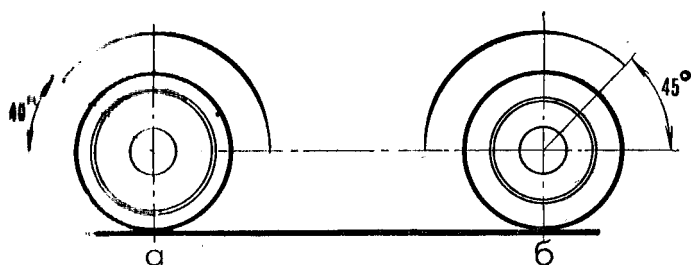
Положение щитков колес: а — переднего; б — заднего
